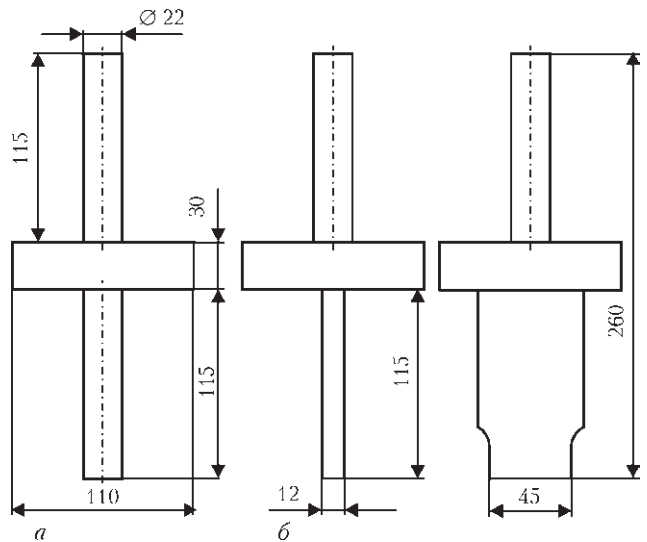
Чертеж модельного образца сварного соединения шпильки крепления плит БМП с верхним поясом тавровой балки с цилиндрической (а) и призматической (б) захватными частями (первая серия образцов)
